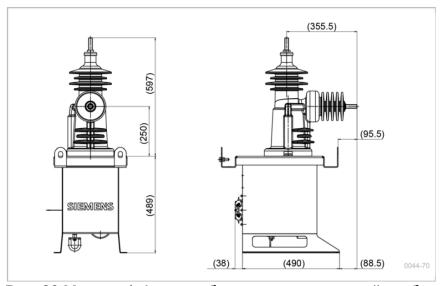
Модель 1-фазного блока переключателей - габаритные размеры
